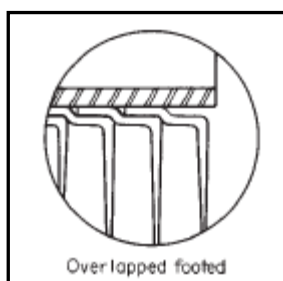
Construcción de recorrido solapado del tubo aleteado
